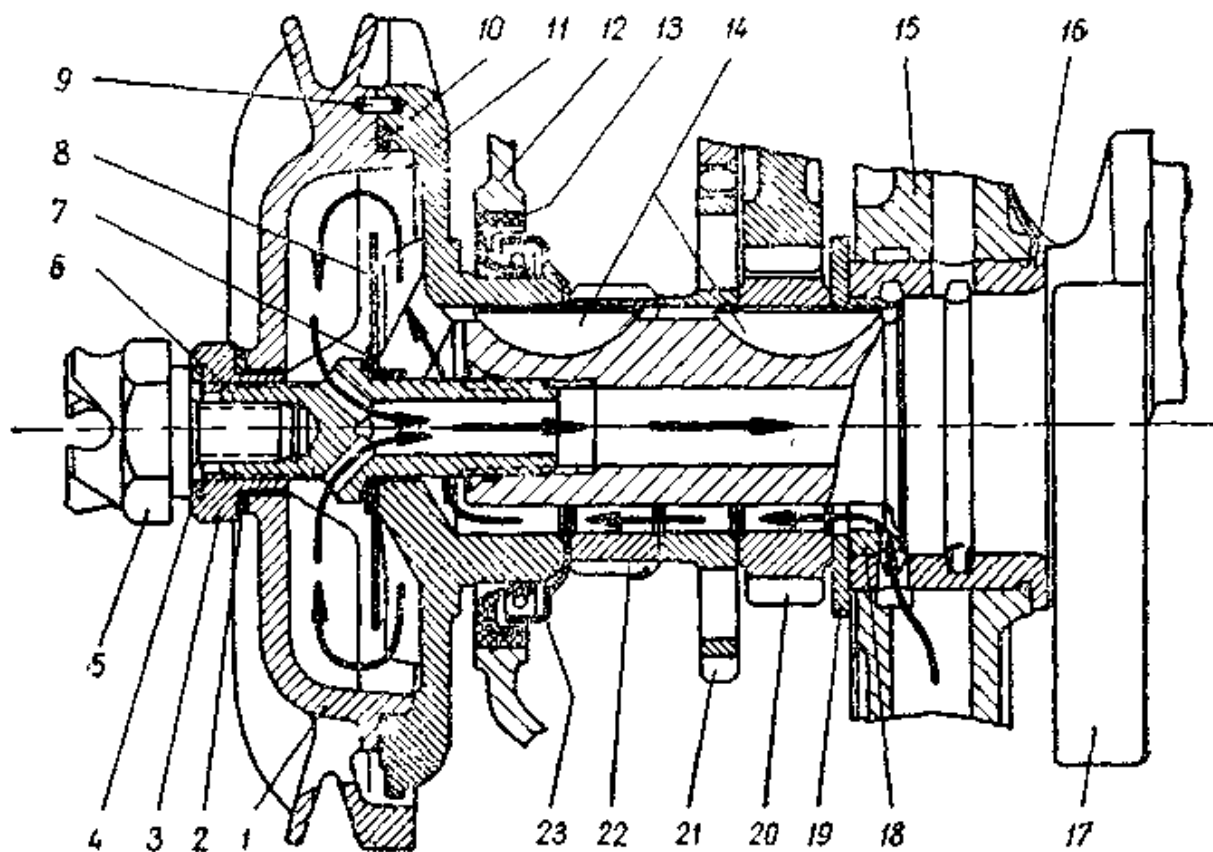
Центрифуга и передний коренной подшипник коленчатого вала
